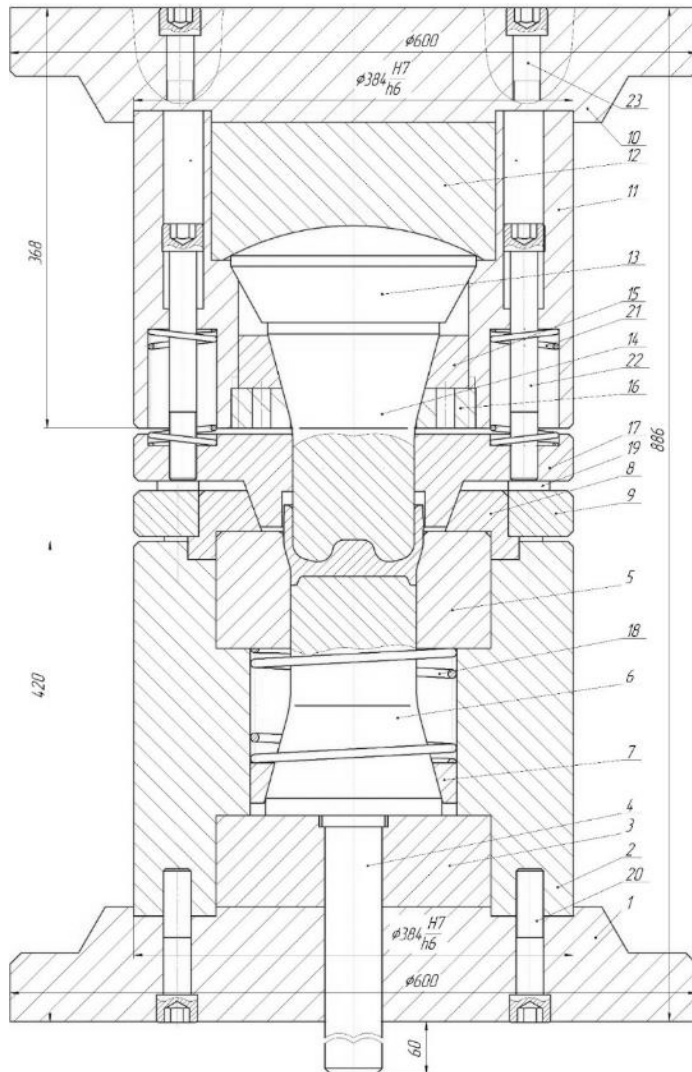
Конструкція штампу для гарячого зворотного видавлювання
